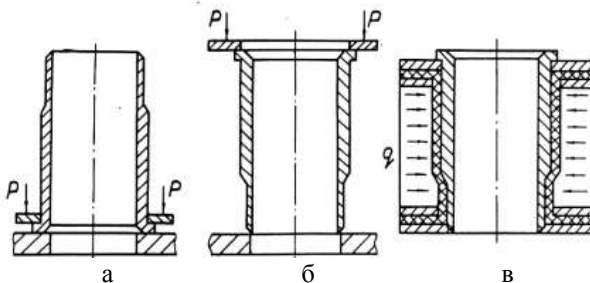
Способи кріплення циліндрів: а - кріплення за буртик циліндра; б - кріплення з притиском по торцях циліндра; в - кріплення циліндра по зовнішній поверхні в гумовій діафрагмі
